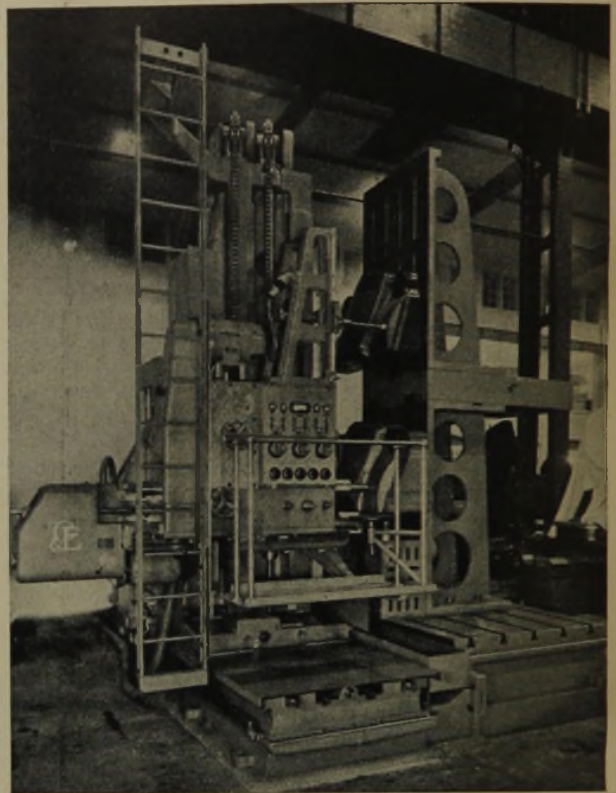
Kopierfräsmaschine mit elektrischer Fühlersteuerung zur Bearbeitung von Prefwerkzeugen für die Automobilindustrie
